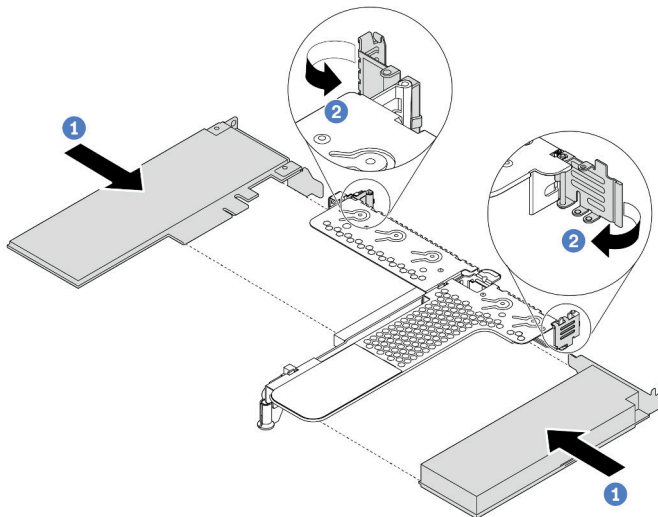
Instalação do adaptador PCIe no conjunto de placa riser LP-FH
